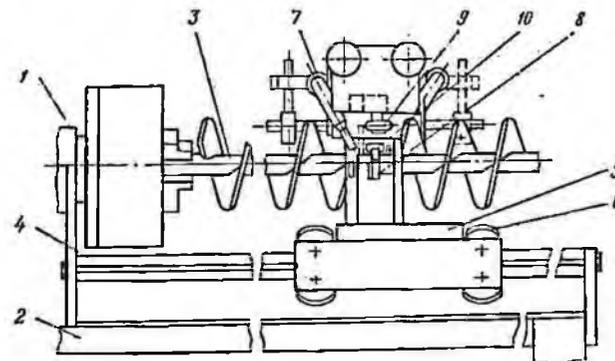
Устройство для изготовления шнеков с использованием автоматической электродуговой сварки:
